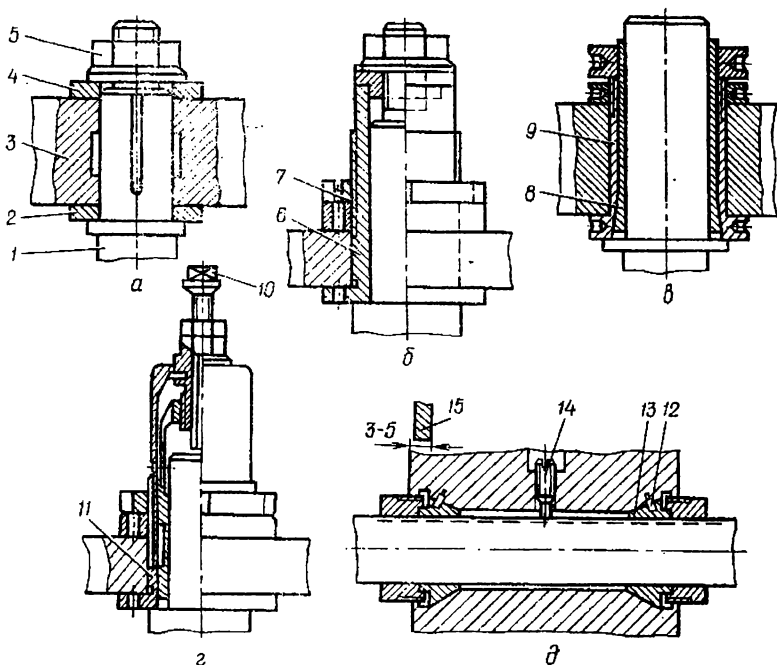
Способы крепления насадных фрез на шпинделе станка:
